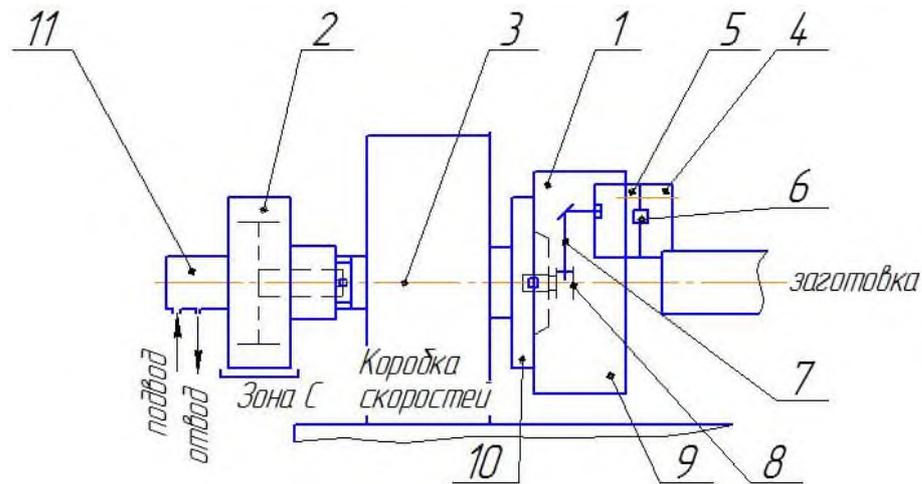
Схема компоновки патрона и силового патрона на станке:
